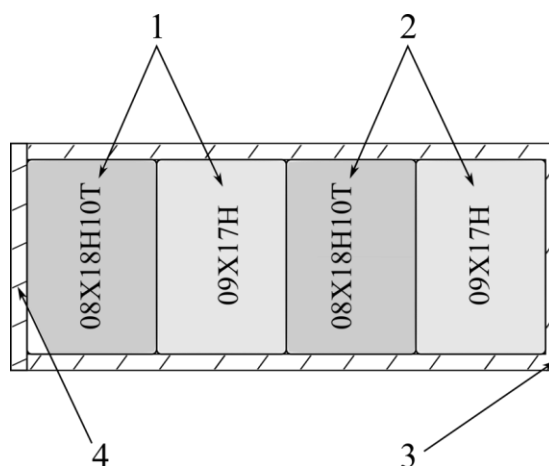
Схема укладки образцов из стали 08X18H10T и 09X17H в контейнер для диффузионной сварки: 1 - сборка 08X18H10T – 09X17H с поверхностями, обработанные соответственно по режиму 1; 2 - контрольная сборка 08X18H10T – 09X17H (без лазерной обработки); 3 - тонкостенный контейнер; 4 - крышка контейнера.
